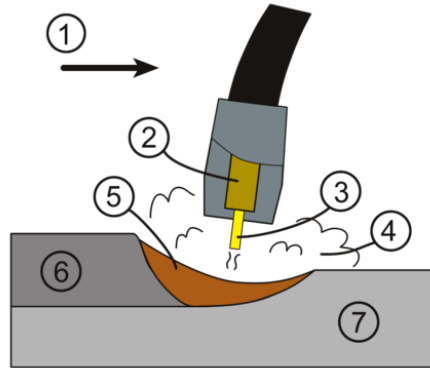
Diagrama de equipo de soldadura MIG
